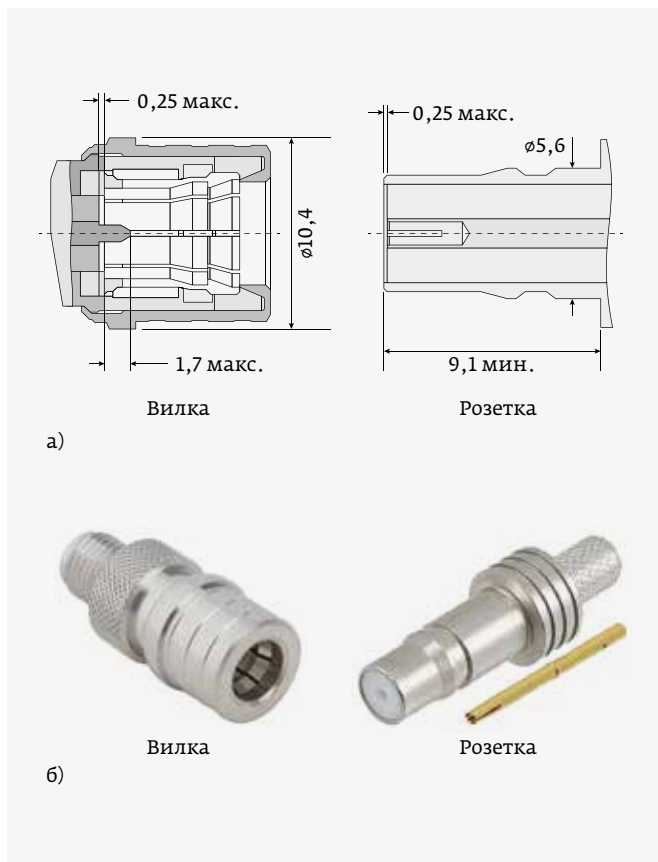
Интерфейс (а) и внешний вид (б) соединителя QMA
